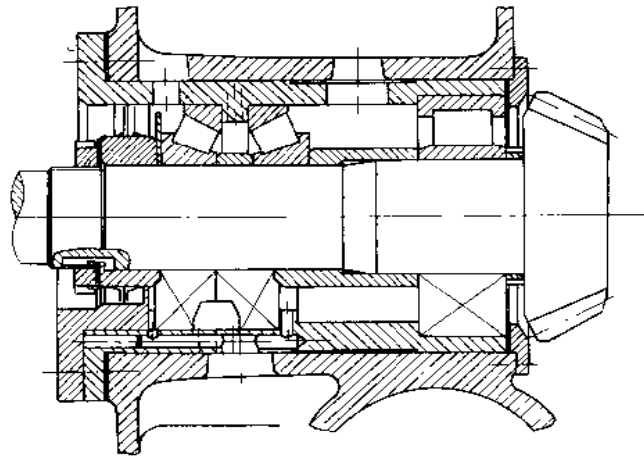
以两套锥形滚柱轴承和一套圆筒形滚柱轴承为支承的齿轮轴
